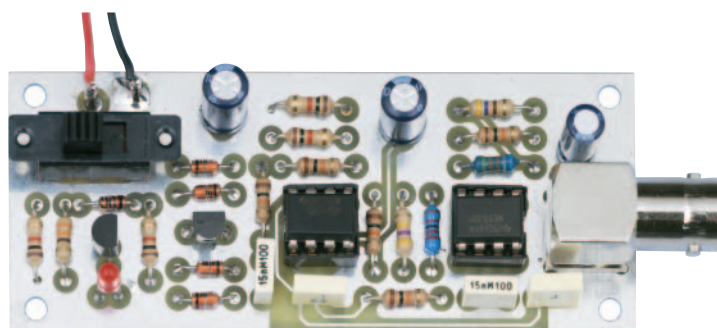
Foto del montaggio del calibratore LX.1691. A sinistra è visibile il corpo dell'interruttore di accensione e, a destra, quello del connettore BNC di uscita.
